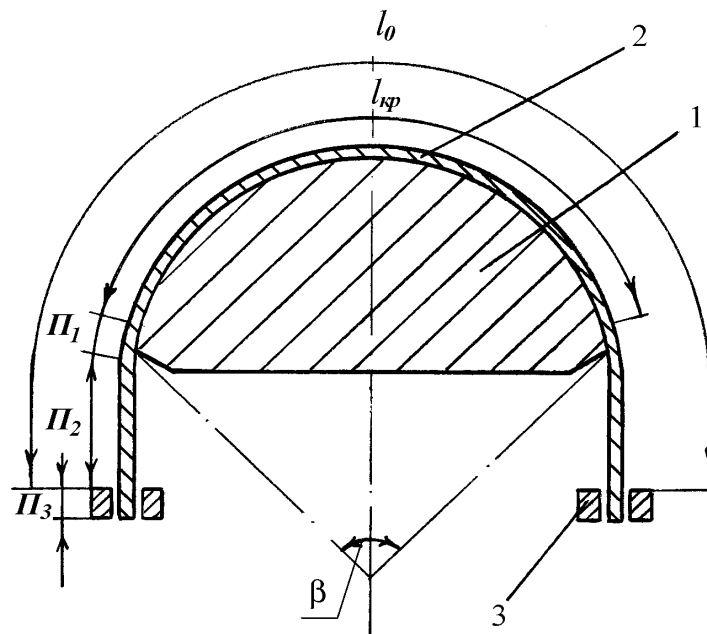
Схема визначення довжини заготовки: 1 – пуансон для обтягування; 2 – листовая заготовка; 3 – затискачі
